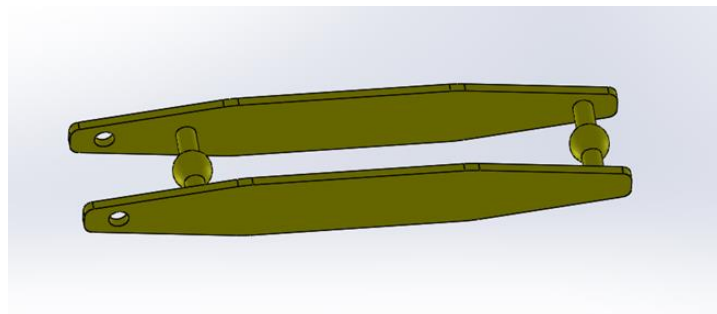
Barra o struts laterales, FUENTE: SOLIDWORKS
